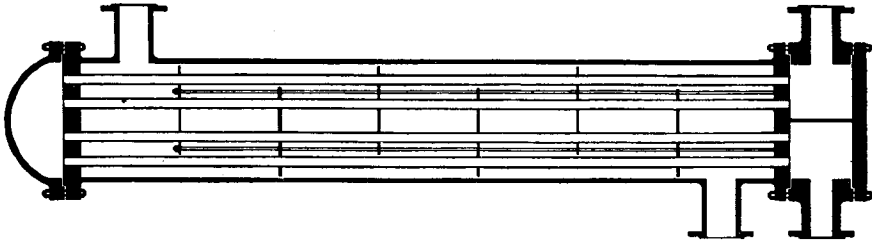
Intercambiador 1-2 de cabezal fijo. (*Patterson Foundry & Machine Co.*)
